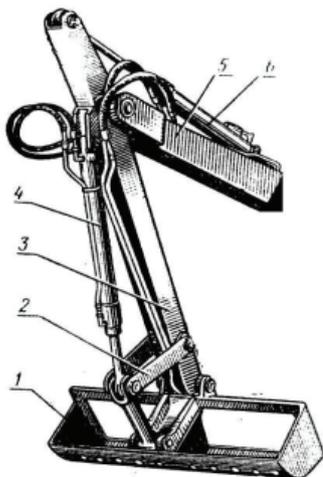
Общий вид поворотного ковша с перегородкой: 1 — ковш с перегородкой; 2 — раскос; 3 — рукоять; 4 — гидроцилиндр поворота ковша; 5 — стрела; 6 — гидроцилиндр управления рукоятью
